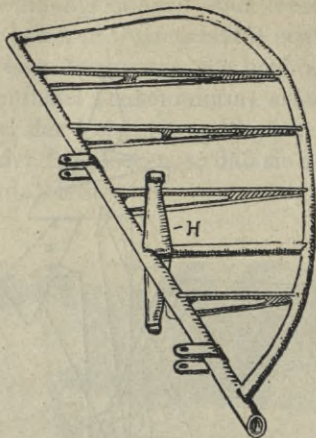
Stahlrohr-Rahmen einer Steuerfläche. (*H* = Hebel)
